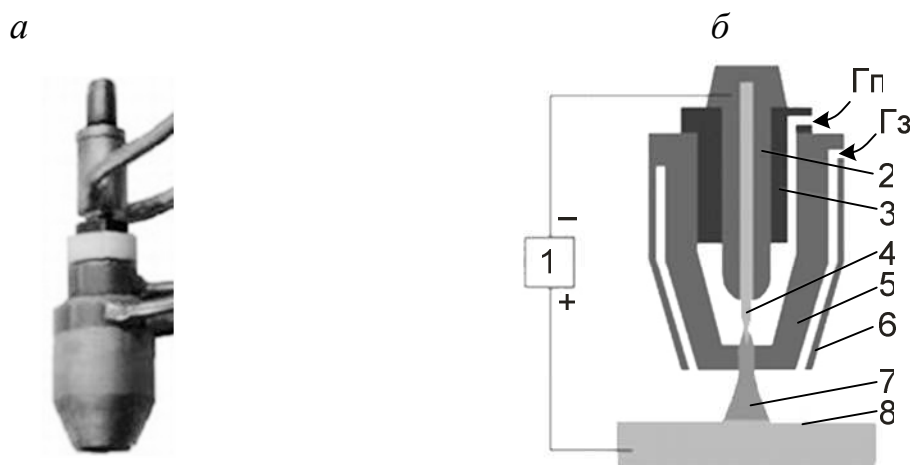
Плазмотрон для сварки прямой полярности:
